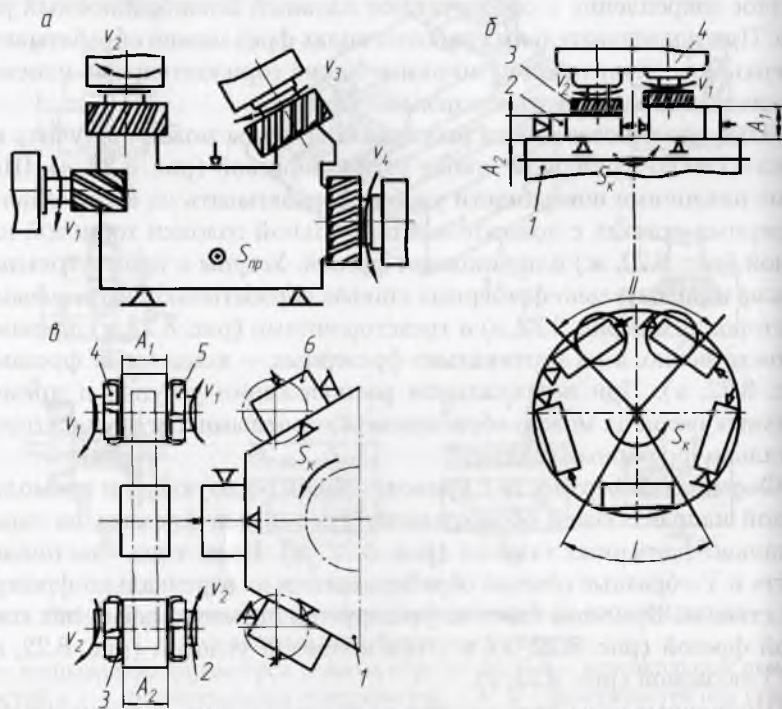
Схемы обработки фрезерованием на продольно-фрезерном (*а*), карусельно-фрезерном (*б*) и барабанно-фрезерном (*в*) станках
